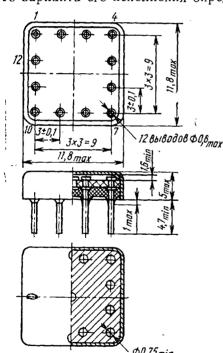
Конструкция металлополимерного корпуса «Тропа»
